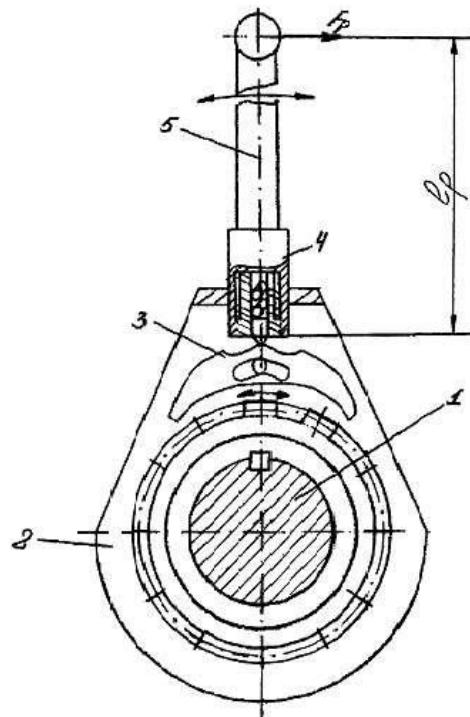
Схема конструкции храповой рукоятки.
